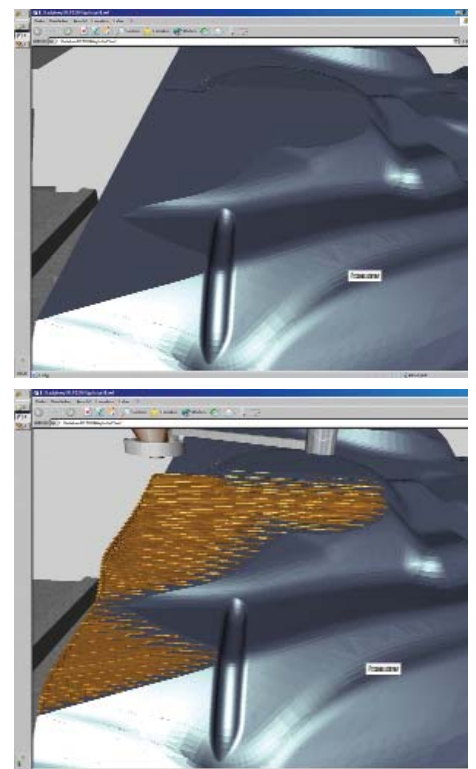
Virtuelles Auftragschweißen an einem Umformwerkzeug
